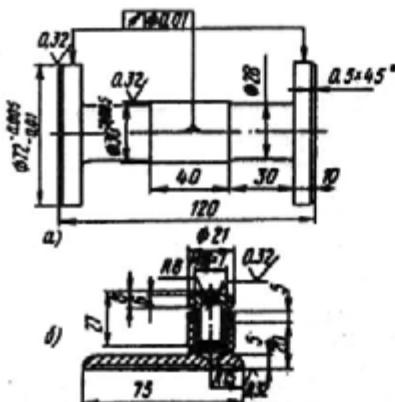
Специальная оправка и микрометрическая стойка для замера монтажного размера в картере редуктора:
